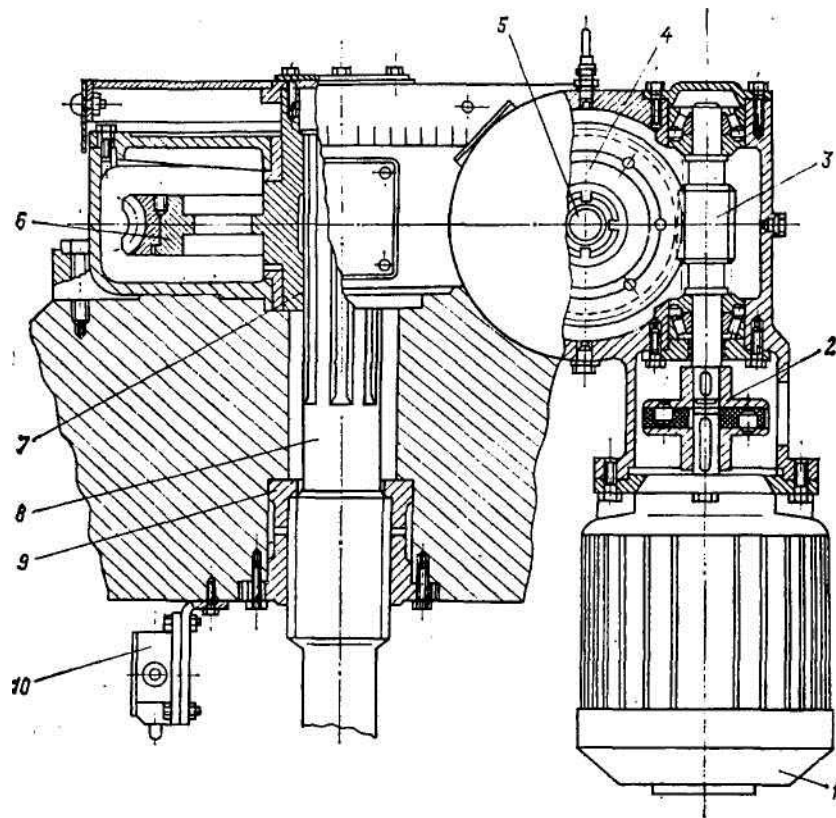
Механізм регулювання міжвалкового зазору каландра:
